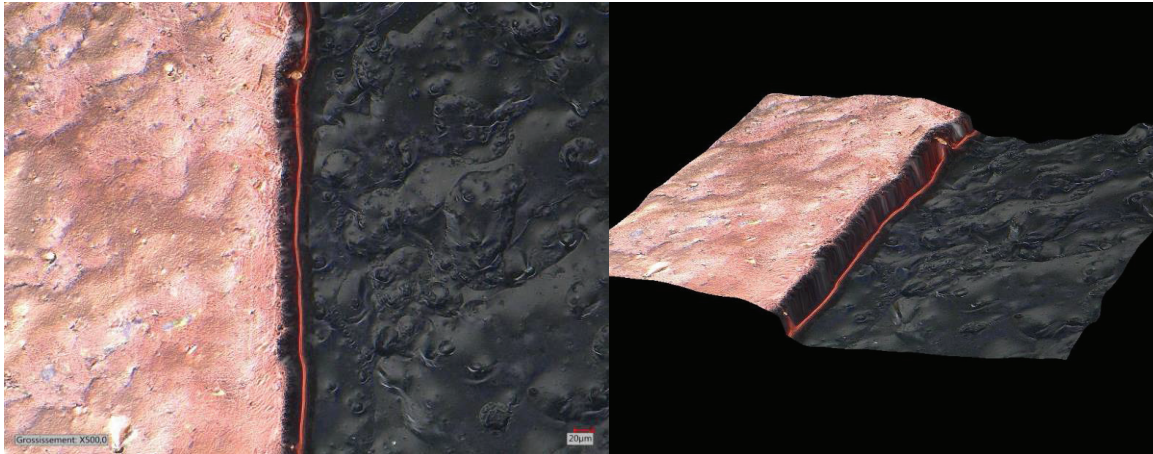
Zoom sur le rebord d'une piste conductrice.
